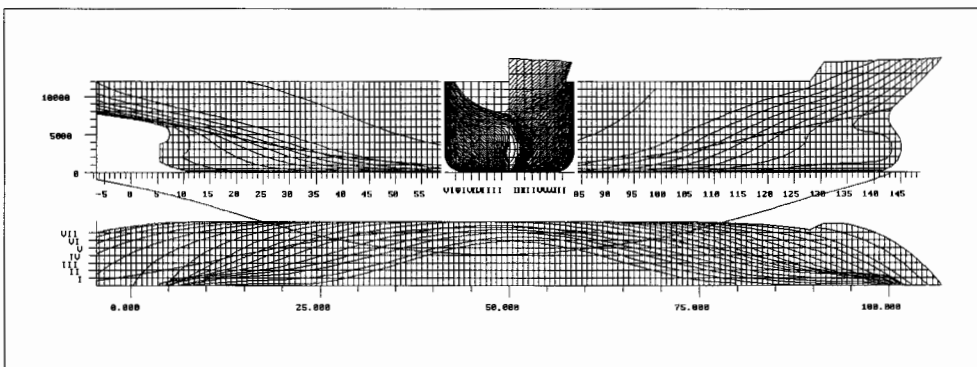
Voorbeeld van een lijnenplan uit Fairway.
